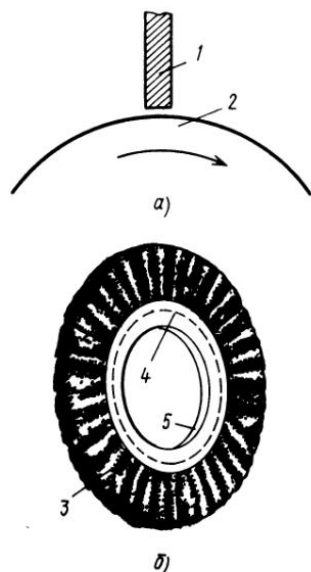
Схема нанесения твердой полировочной пасты на барабан (а) и полировальный диск (б):
